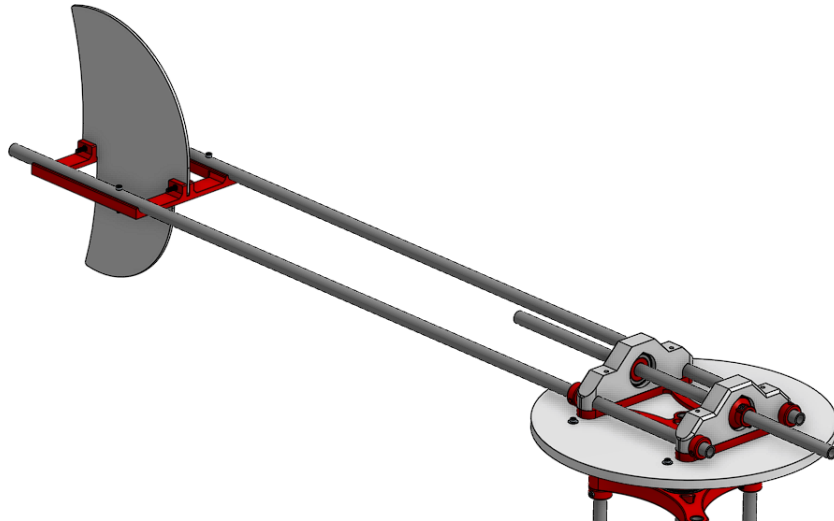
Vista isométrica 1 del ensamblaje de la estructura de la cola en Onshape [fuente: elaboración propia]
